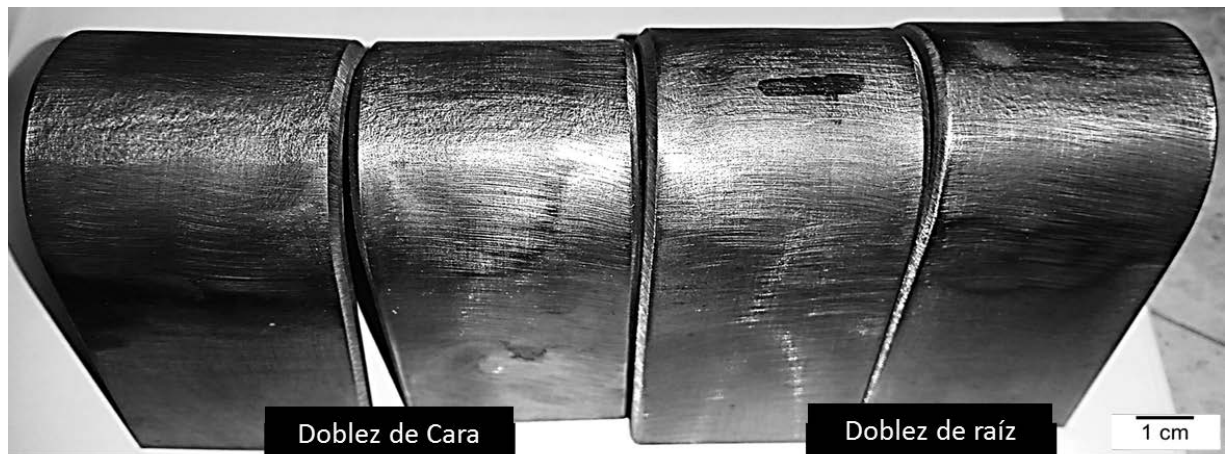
Pruebas de dobles de cara y de raíz de la soldadura 316L.
